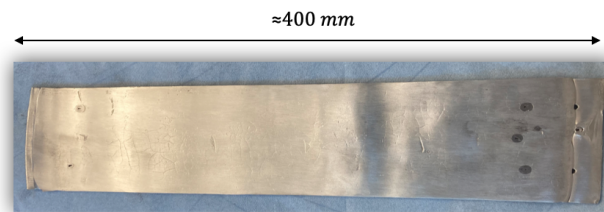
Vue du haut du spécimen empilé en structure sandwich à 5 couches après laminage.
